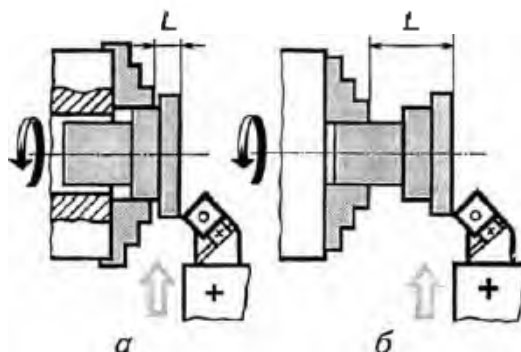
Виліт заготовки з патрона при підрізуванні торця
